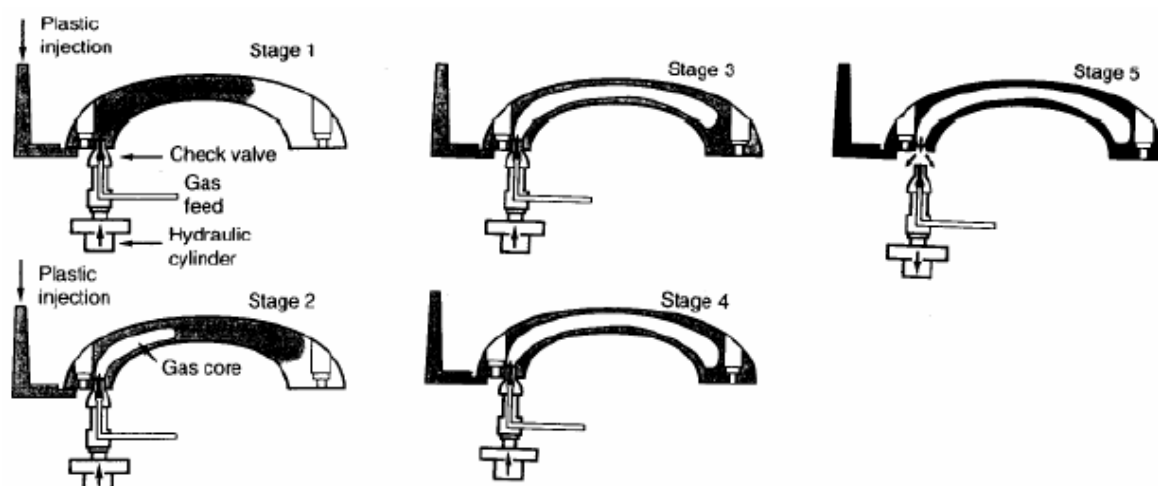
Moldeo con inyección de gas de una manilla de automóvil
